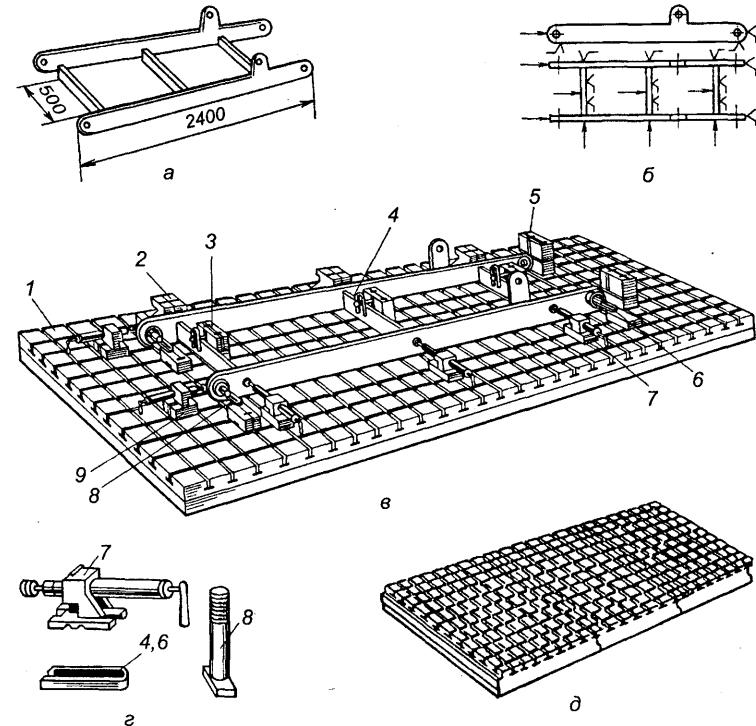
Универсальное сборное приспособление для сварки:
